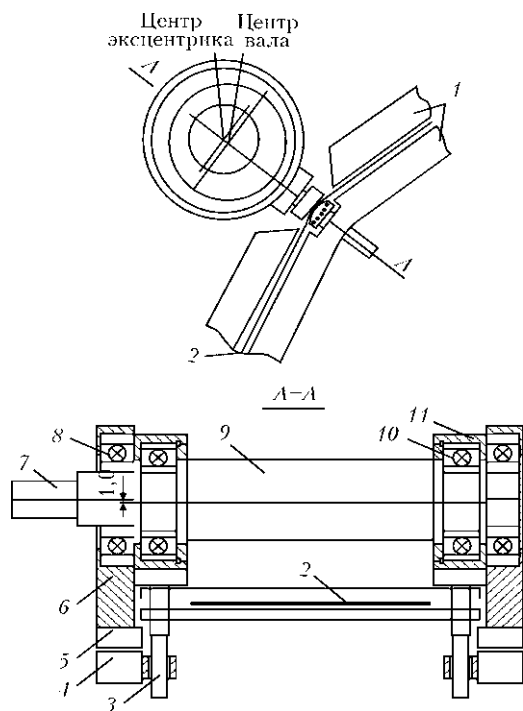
Схема преобразования колебаний торца ленточного электрода из поперечных в продольные: 1 — изогнутое основание; 2 — ленточный электрод; 3 — направляющий болт; 4, 5 — корпуса пластин; 6, 11 — корпуса подшипников; 7 — вал; 8 — подшипник на валу; 9 — средняя часть вала-эксцентрика; 10 — подшипник на эксцентрике
